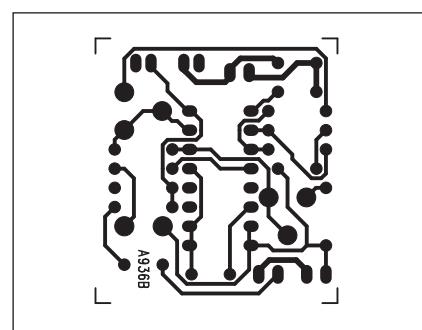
Obrazec desky spojů manažeru zátěže (BOTTOM)
